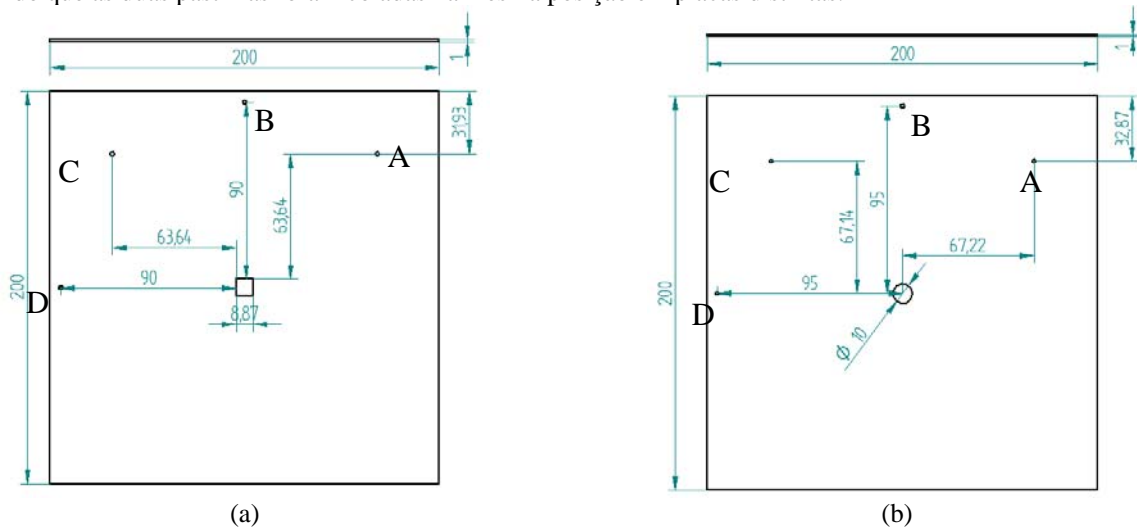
(a) Dimensionamento da placa com pastilha piezolétrica com formato quadrado; (b) Dimensionamento placa com pastilha piezolétrica com formato circular.
